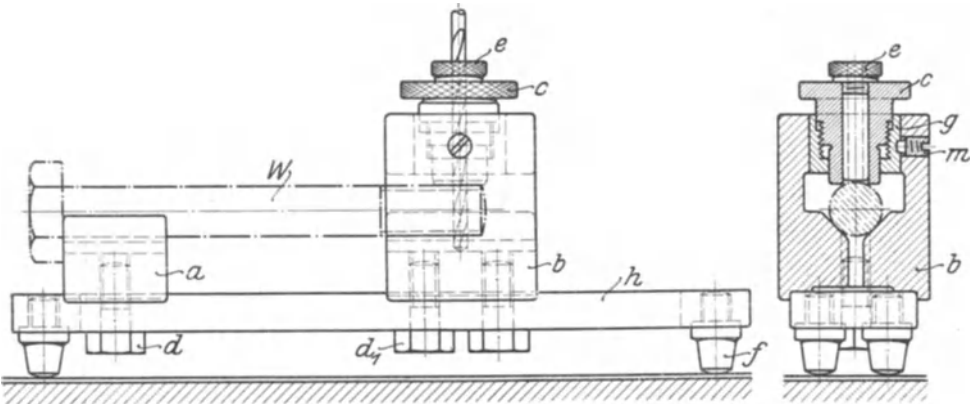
Universalbohrvorrichtung zum Bohren von Splintlöchern in Schrauben.
